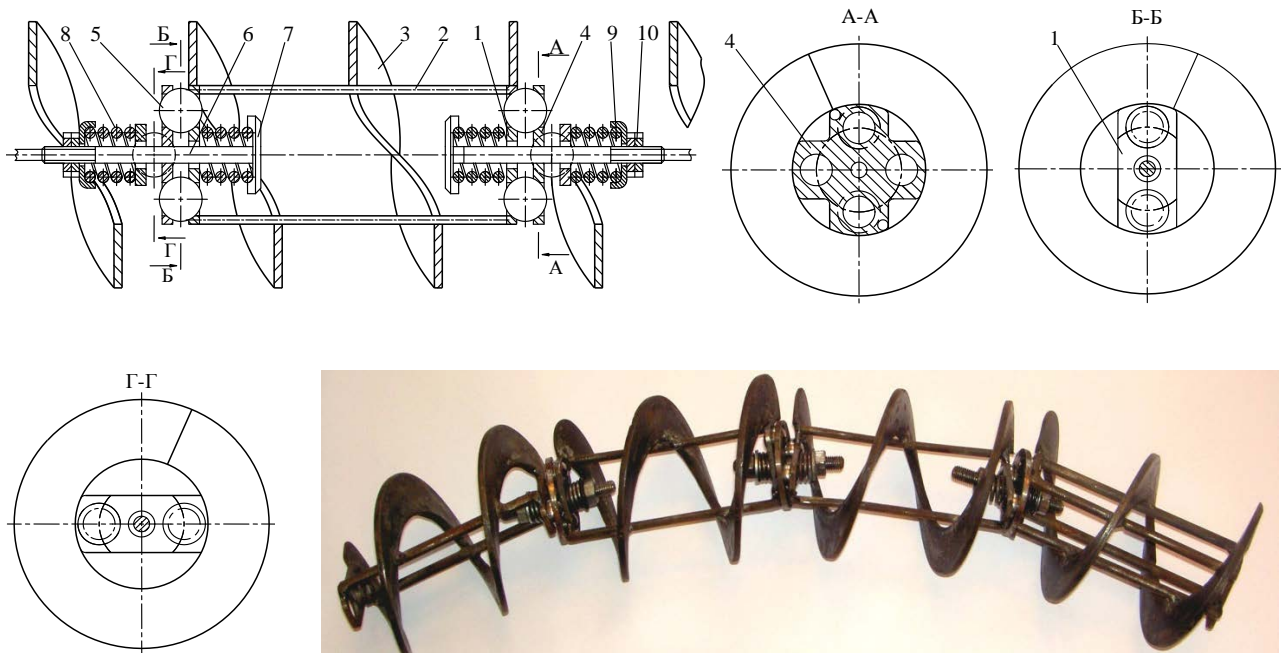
Конструктивна схема та загальний вигляд шарнірного робочого органу гвинтового конвеєра
